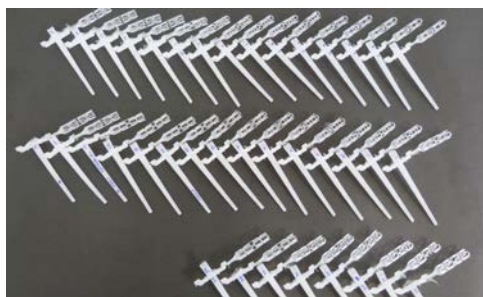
Lote de *stents* com bucha moldados por injeção de PEBD em molde de alumínio.
